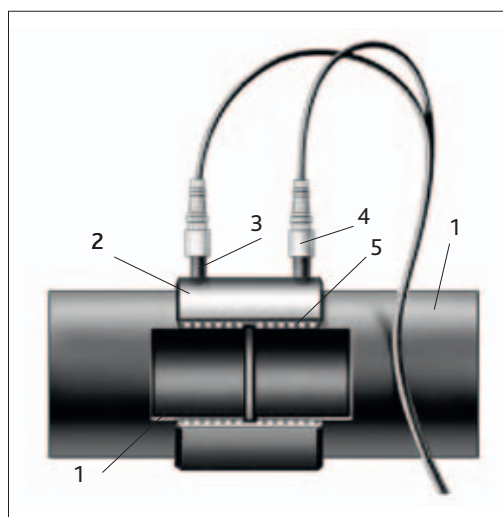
Соединение труб из PE-RT тип II сваркой ЗН: 1 – трубы, 2 – муфта с ЗН, 3 – клеммы токопроводов, 4 – токопроводящие кабели сварочного аппарата, 5 – закладной нагреватель
